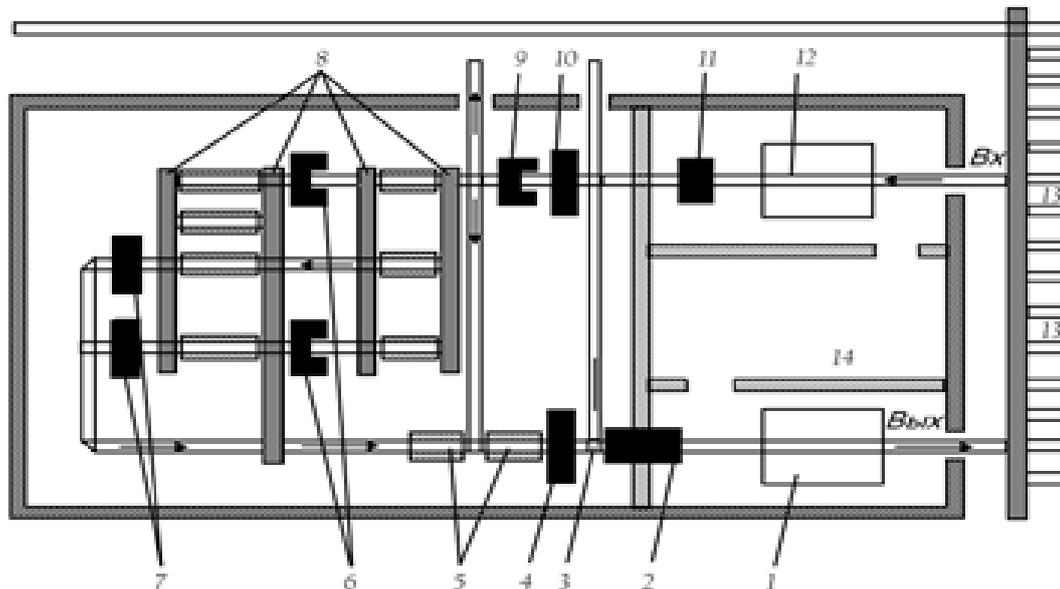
Планировка колесного цеха: 1 – выходной контроль; 2 – площадка для окраски и сушки колёсных пар; 3 – поворотные устройства; 4 – устройство выходного контроля (дефектоскопия, измерение и клеймение колёсных пар); 5 – накопители колёсных пар; 6 – порталные колесотокарные станки; 7 – станки для обтачивания и накатывания шеек и предподступичных частей осей колёсных пар; 8 – устройства для поперечного перемещения колёсных пар; 9 – установка для магнитной и ультразвуковой дефектоскопии; 10 – стенд для измерения колёсных пар; 11 – моечная машина; 12 – стенд демонтажа роликовых букс; 13 – колёсный парк; 14 – участок ремонта и комплектования подшипников и буксовых узлов
